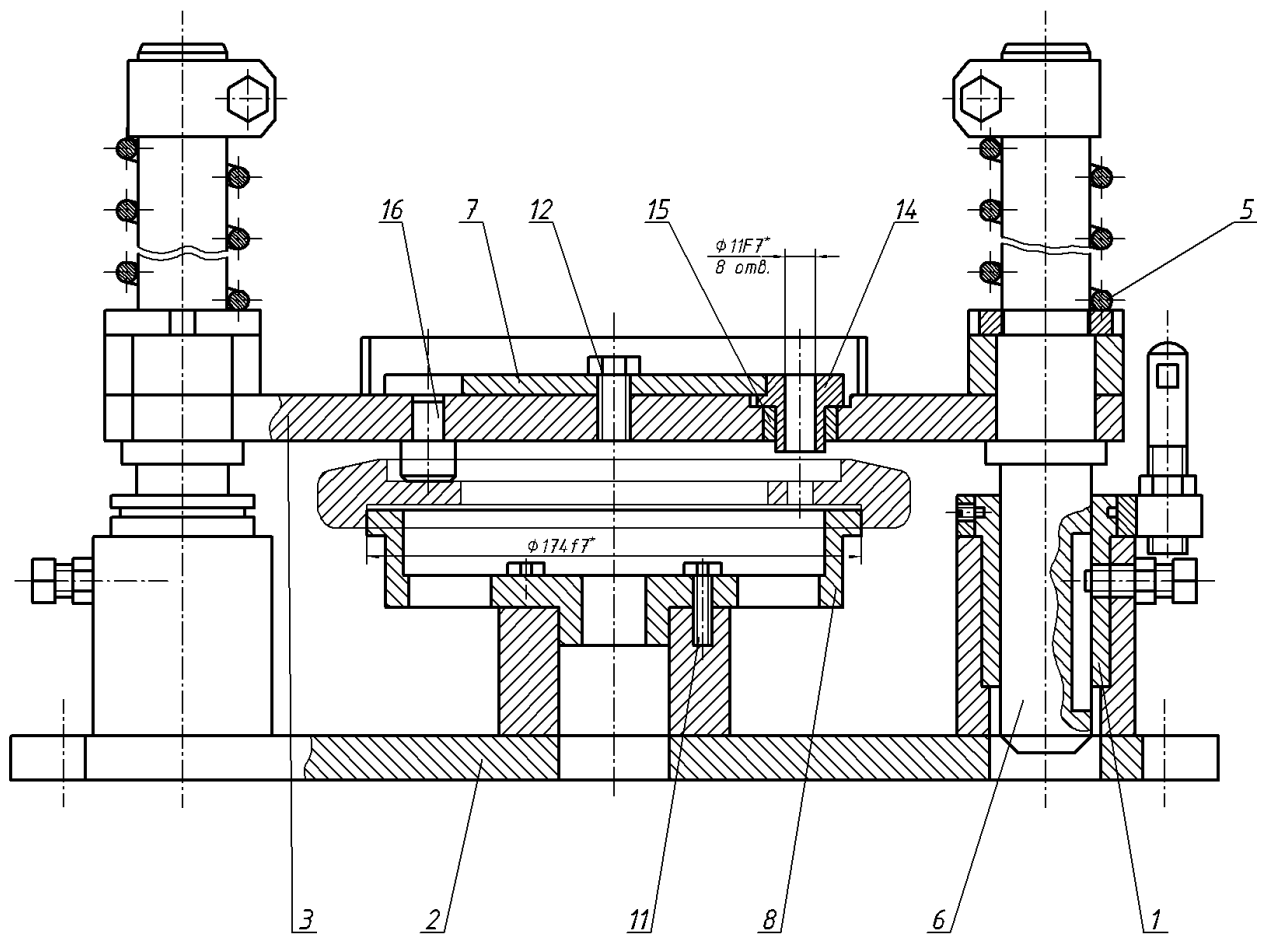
Кондуктор для свердління 8-ми отворів Ø11
